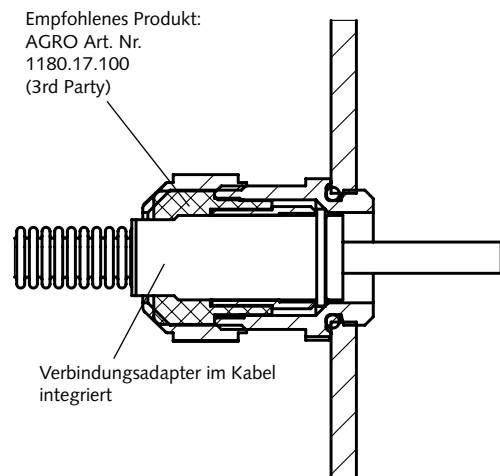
Kabel mit hermetisch dichtem Wellschlauch
